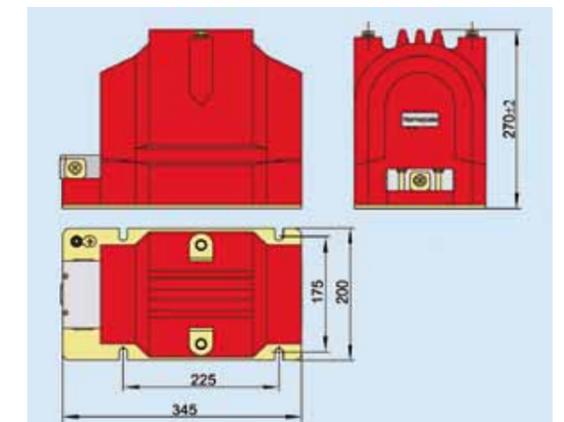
Внешний вид и монтажные размеры трансформатора напряжения JDZ11-10A
